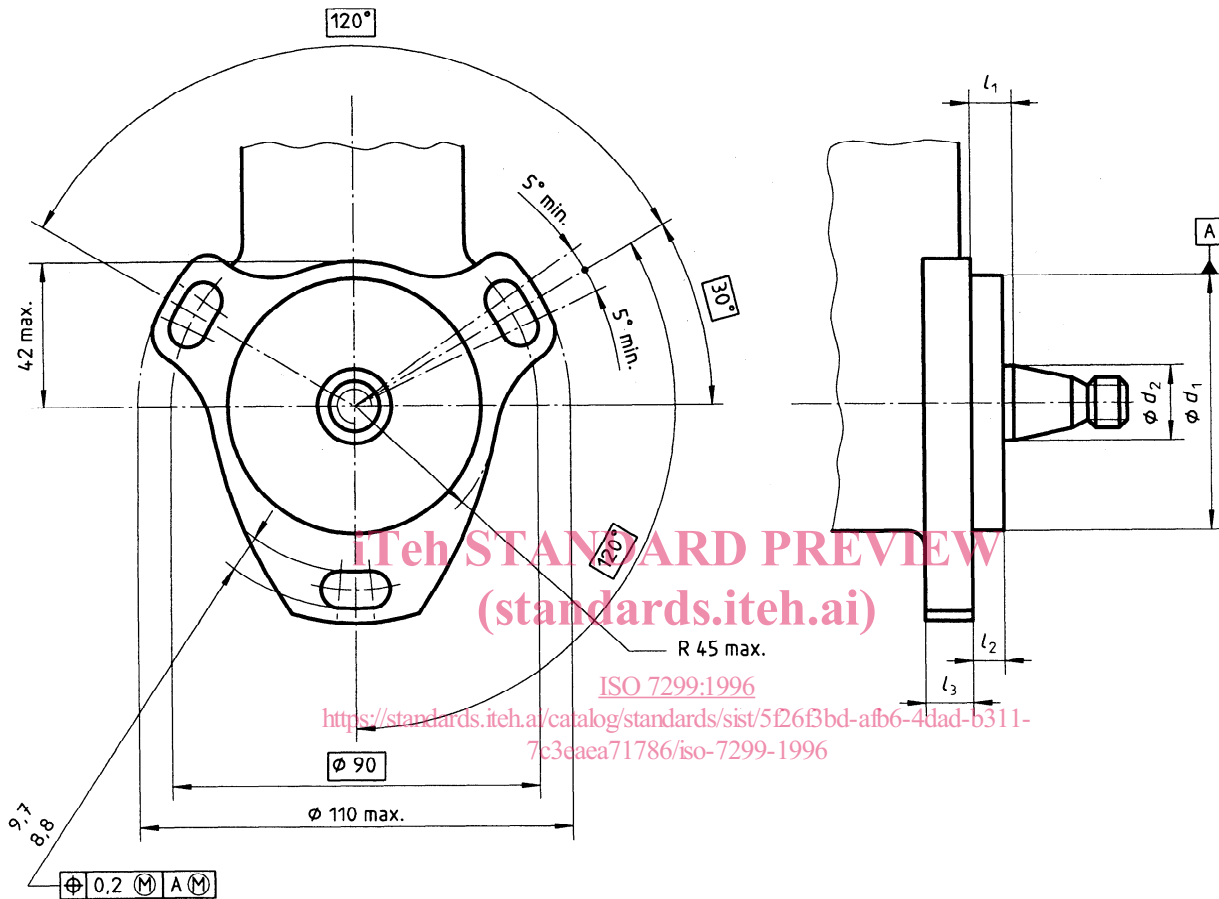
Pompes d'injection de carburant en ligne — Bride de montage de type 4
